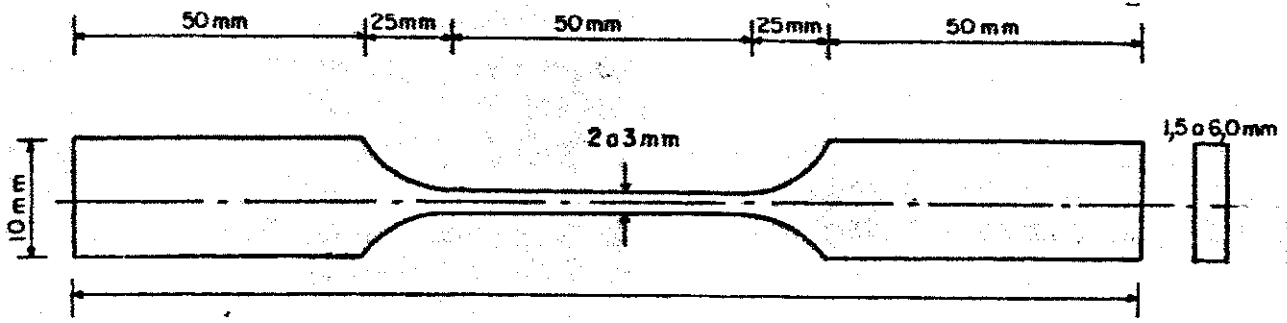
Dimensões do corpo de prova para o ensaio de tração
